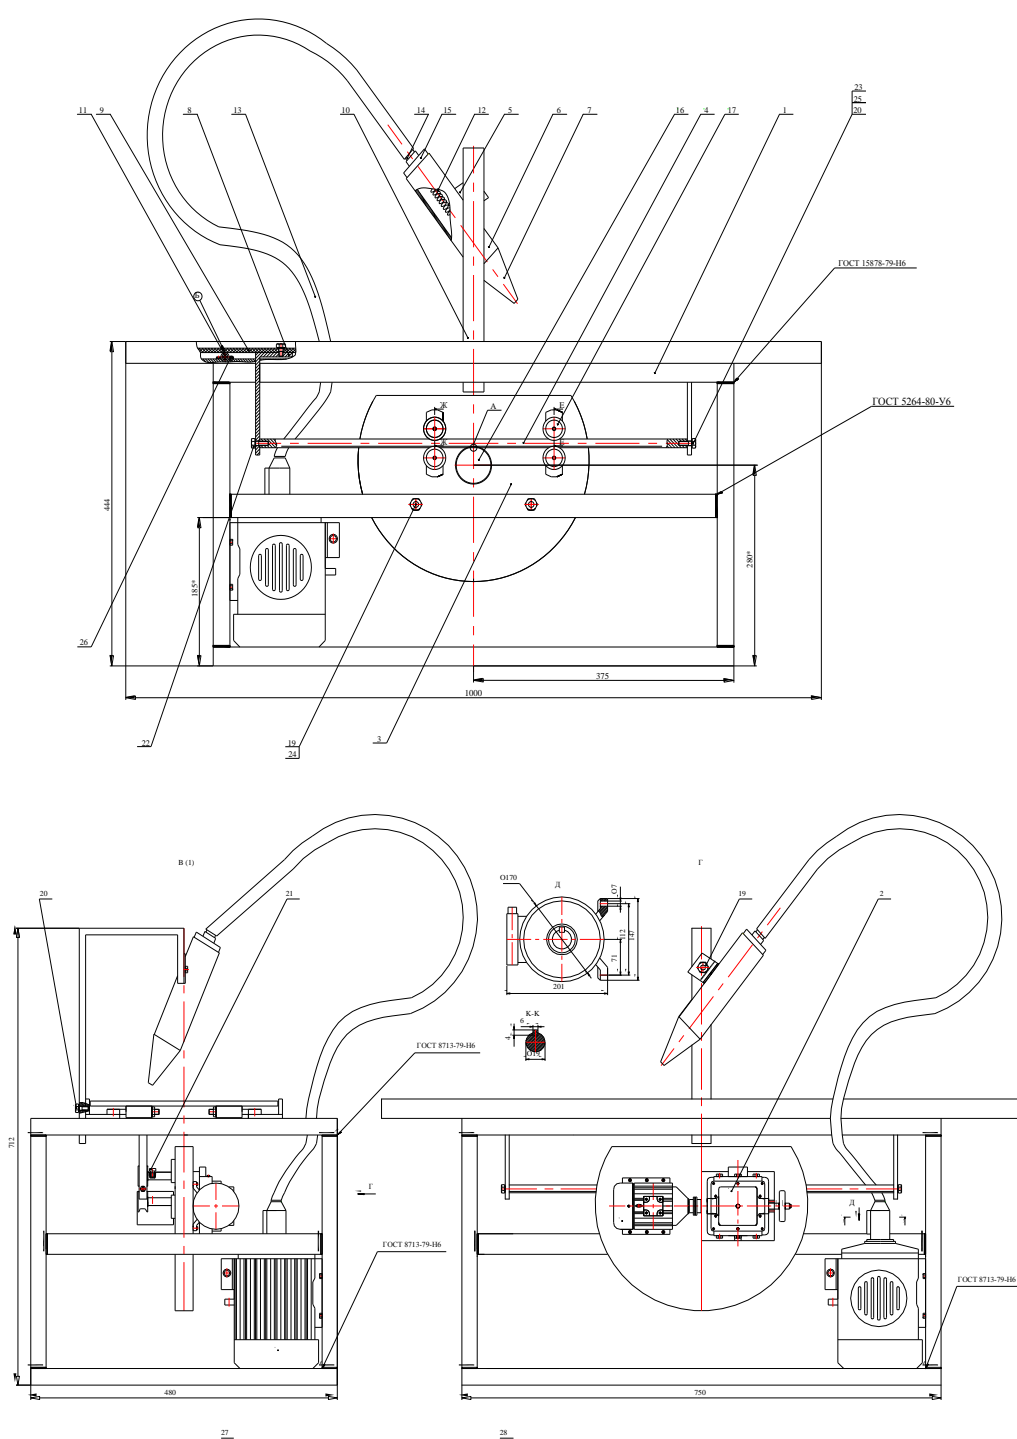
Зварювальний пристрій полімерних матеріалів для легкої промисловості
